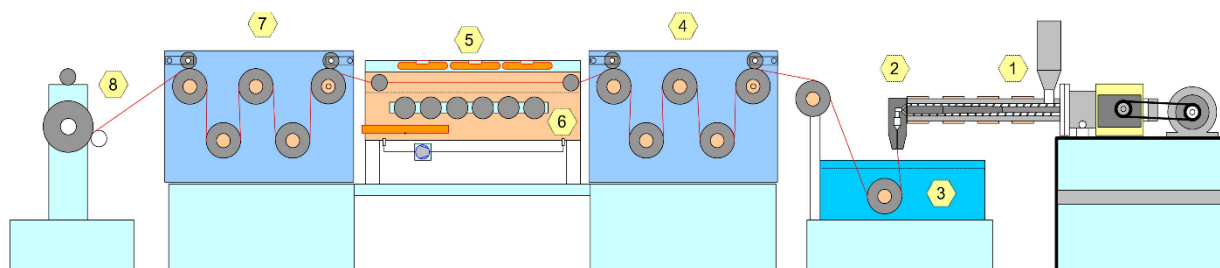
Лабораторний витяжний стенд п'ятивальцевий: 1- екструдер; 2- головка; 3- ванна для охолодження; 4-, 7 – п'ятивальцева система витягування; 5- нагрівачі; 6- утримуючі ролики; 8 – намотчик мононитки
